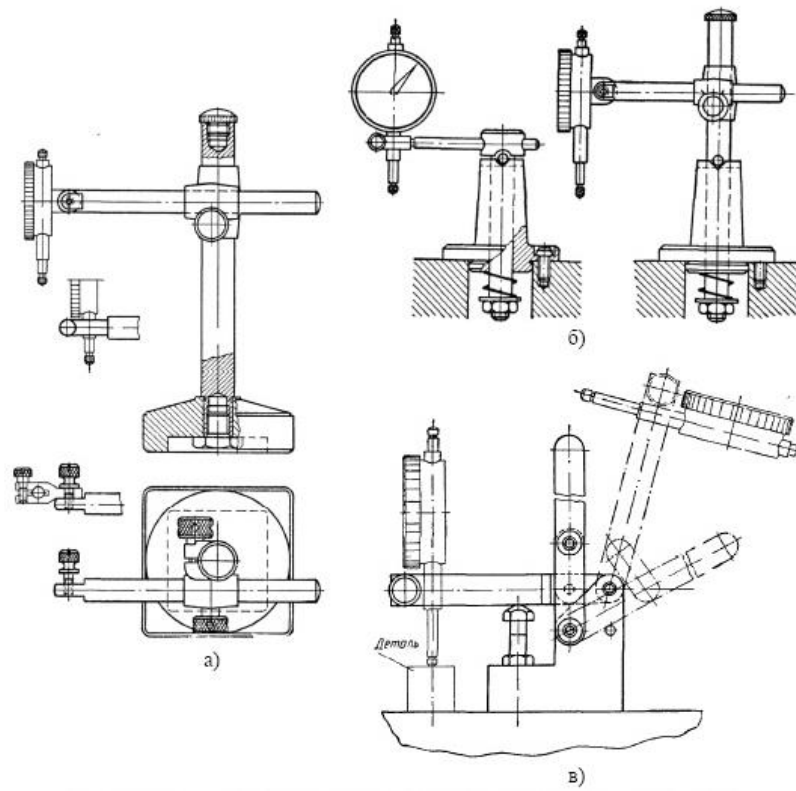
Варіанти конструкції штативів для установки індикаторів і вимірювальних головок: універсальний штатив для індикатора (а), поворотний штатив (б), відкидний штатив (в)
